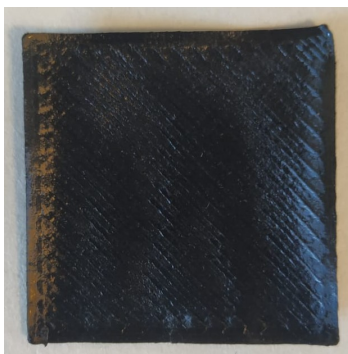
Placa impresa boq.0,6mm, ec=0,15mm
